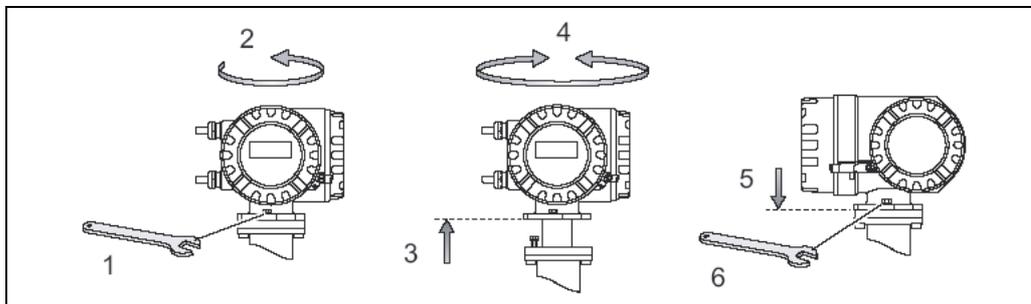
Поворот корпуса трансмиттера (полевой корпус из алюминия)
